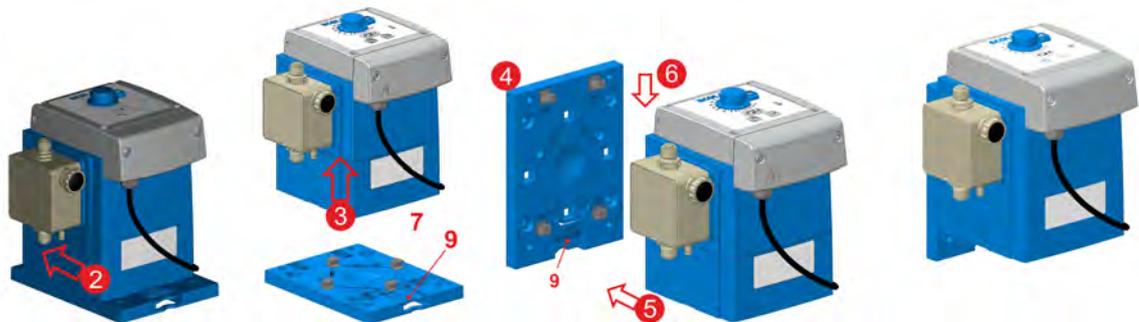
Cambio de montaje de pie (p. ej., sobre suelo, consola o garrafa) a montaje en pared (suspendido)
